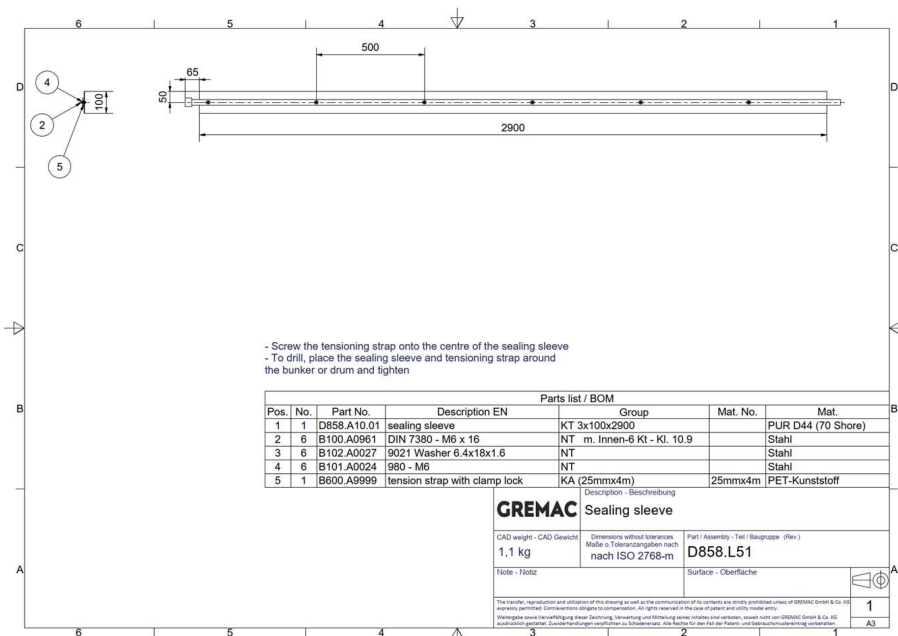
Technische Zeichnung Dichtmanschette D858.L51
